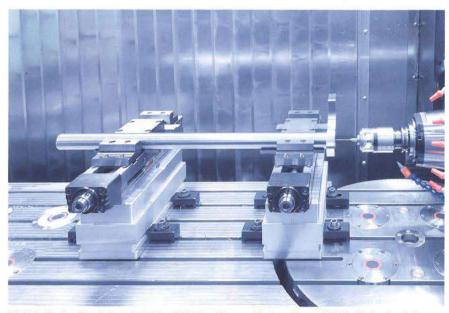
In Eschweiler sind auch 5-Achs-CNC-Maschinen verfügbar, die speziell für die Hartbearbeitung ausgelegt sind. Bild: Rodriguez
